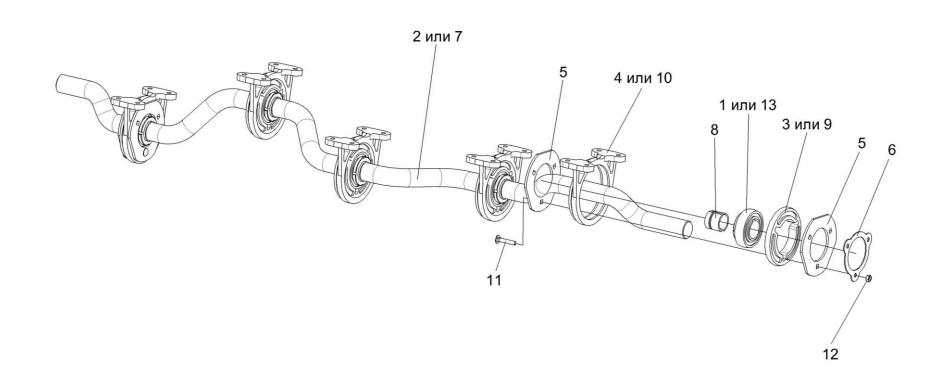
Вал коленчатый ведомый КЗК-12-0212080
